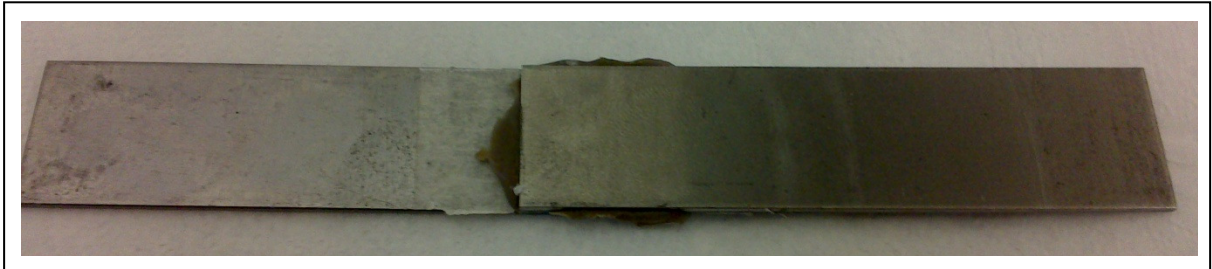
Corpo de prova de junta rebitada – Ensaio de tração pura
